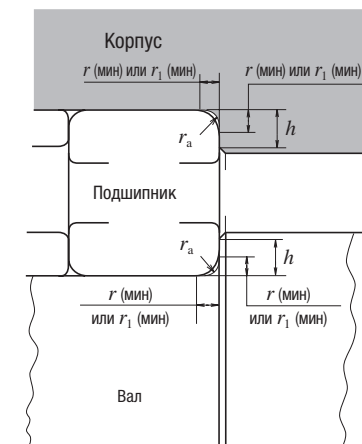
Размеры фасок, радиусы галтели вала и корпуса и высота заплечика
